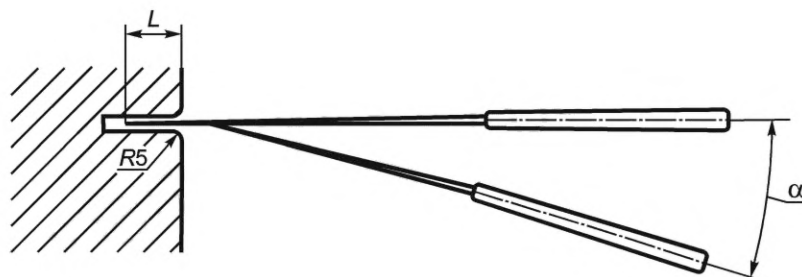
Проверка изгибом упругости клинков ножей, кроме детских, для масла и рыбы и рабочих частей лопаток-шпателей
